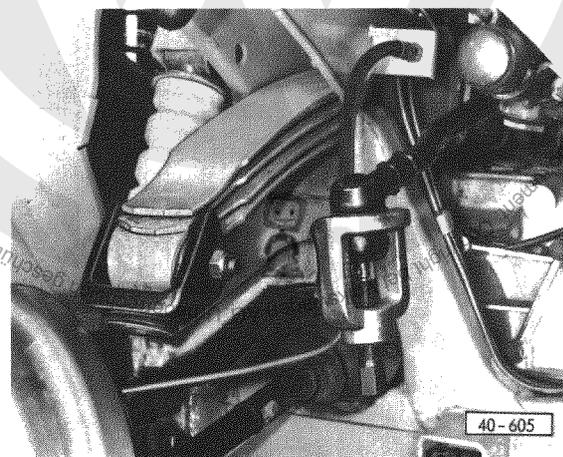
Gummimetallager für Blattfeder aus- und einpressen
